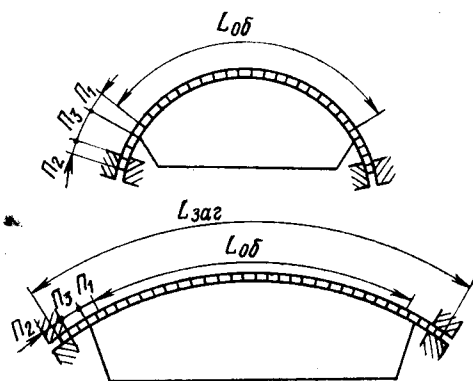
Схема определения длины заготовки обшивки двойной кривизны, изготавливаемой обтяжкой.
